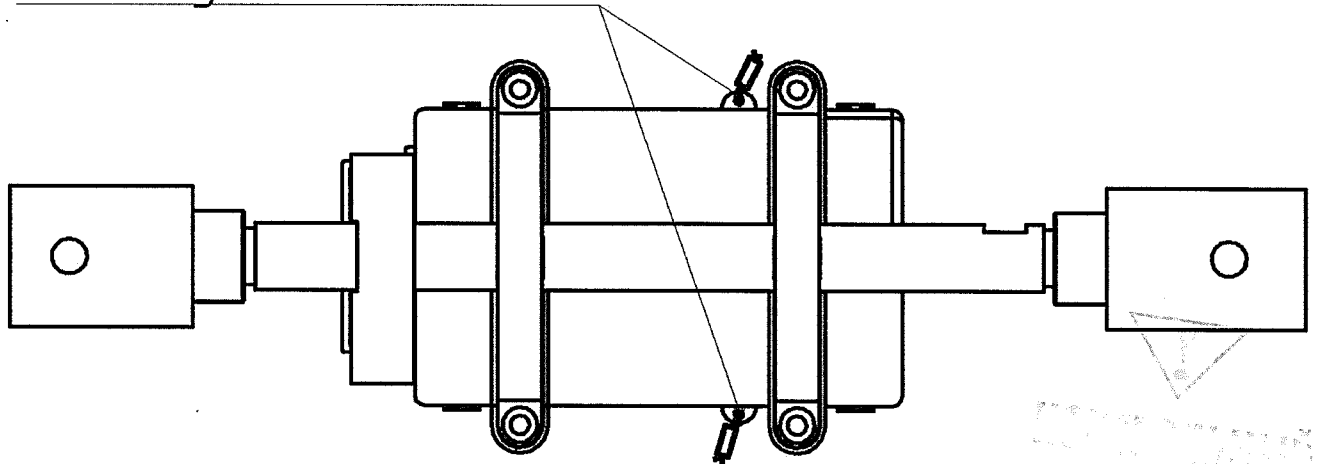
Место установки пломб поверителя на ДИЭ (вид сверху)
